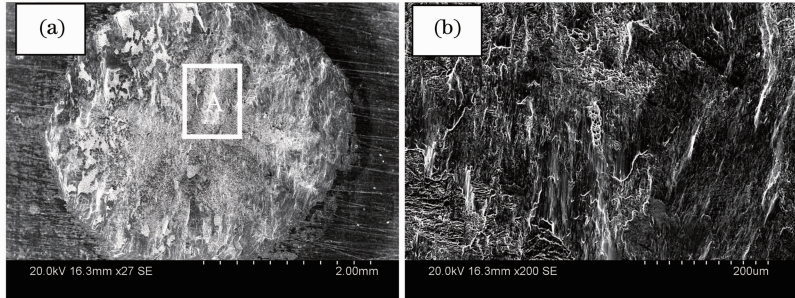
激光点焊接头断口形貌。(a) 宏观形貌；(b) 焊点中心部位
